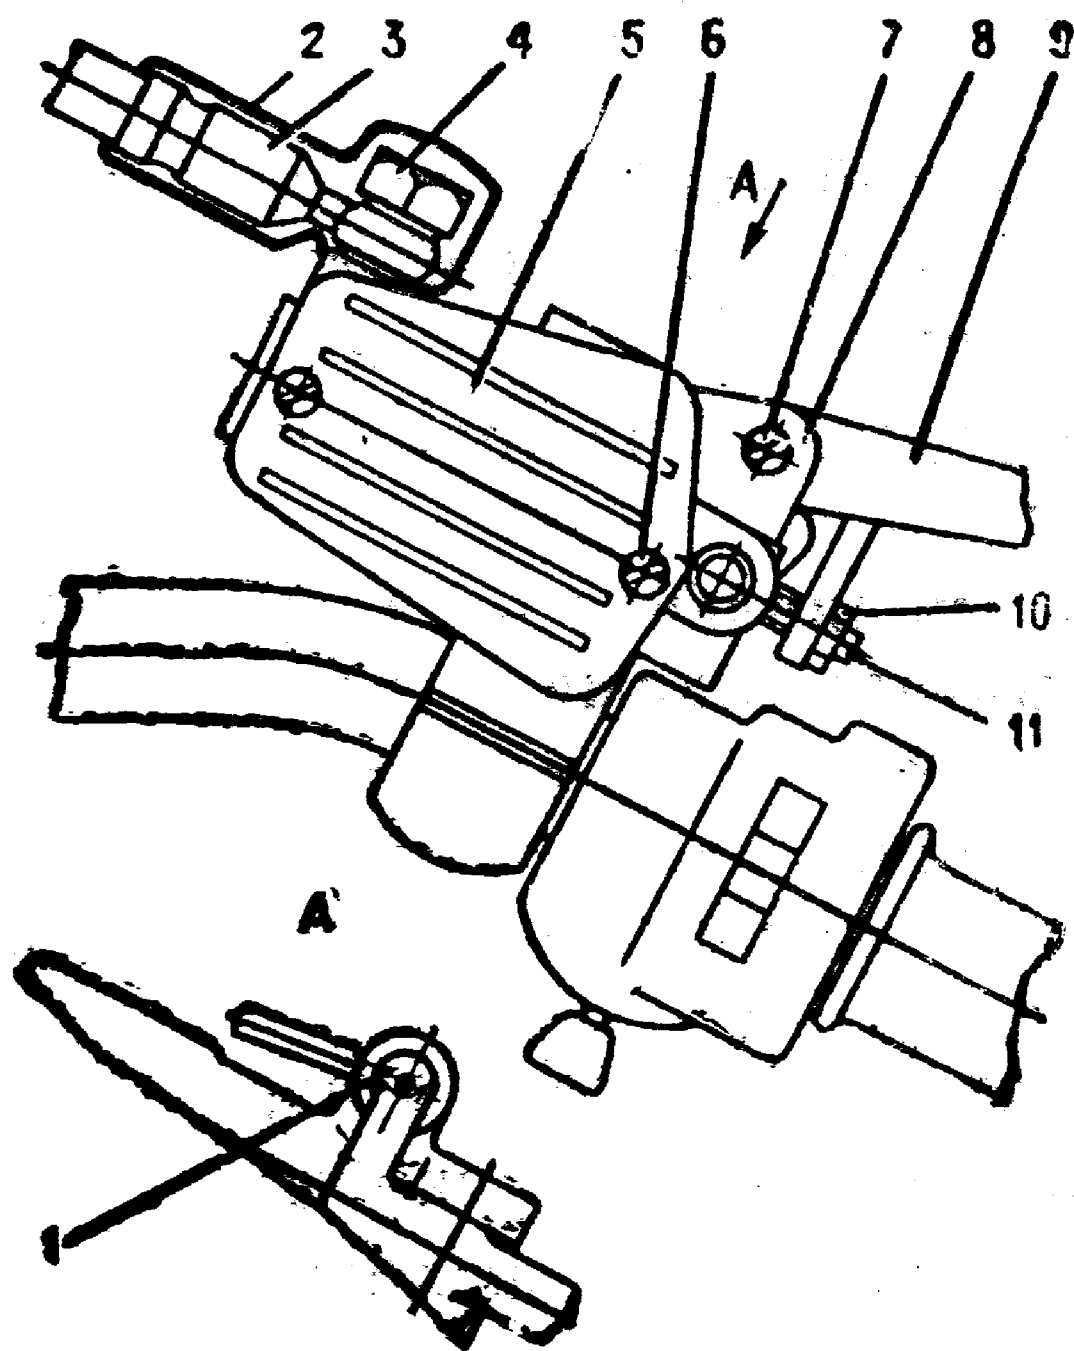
Тормоз дисковый колеса переднего:
